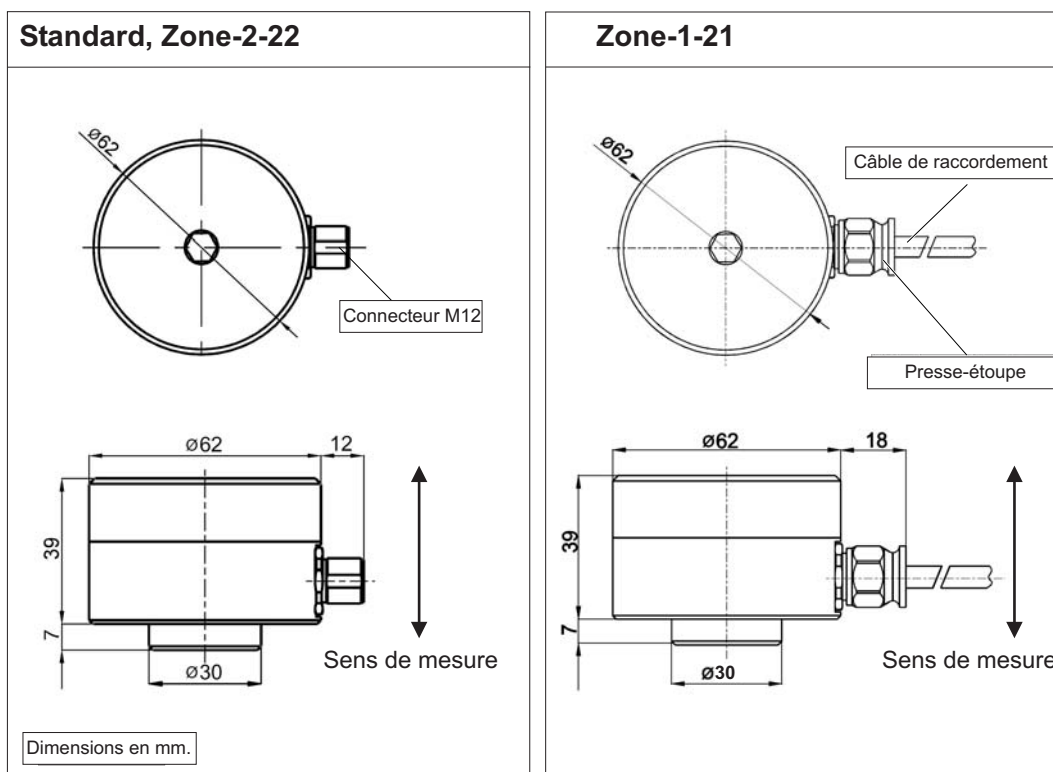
Dimensions du boîtier et sens de mesure : Standard, Zone-2-22. Fig. 4 : Dimensions du boîtier et sens de mesure : Zone1-21
